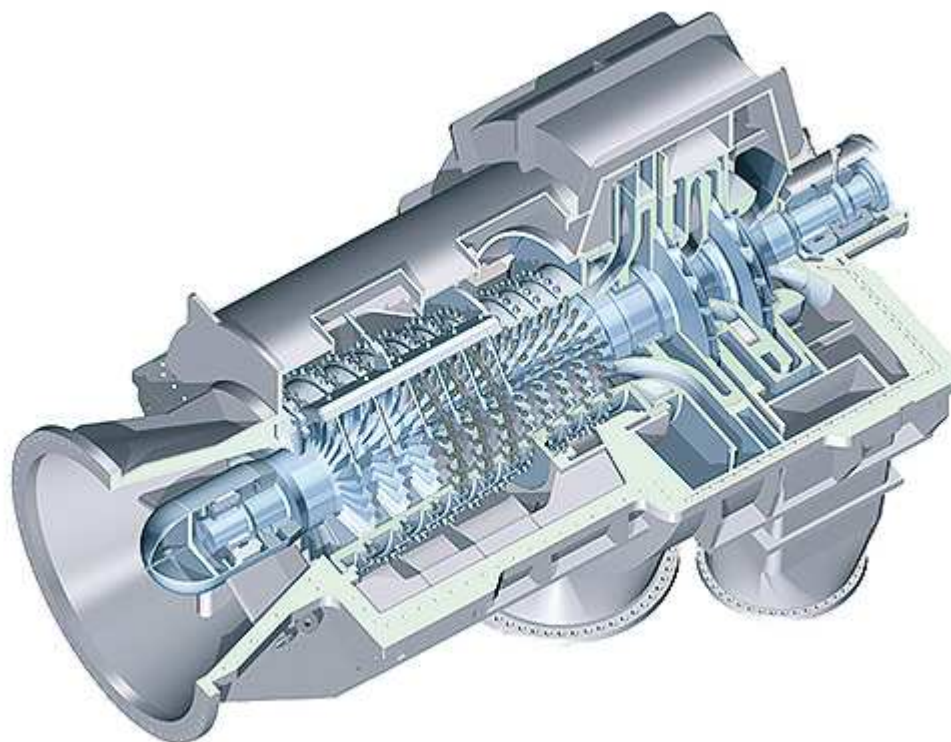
Exemplo de máquina rotativa: Turbina a vapor – Fonte: Siemens
